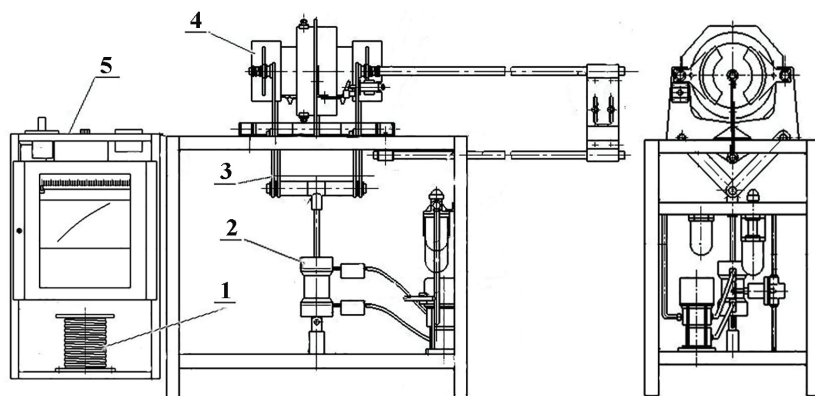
Общий вид опытной установки сварки трубных заготовок внахлест:
